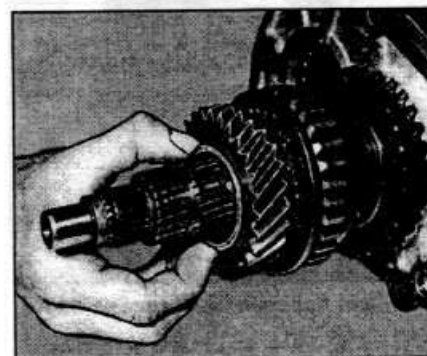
Снятие стопорной шайбы и двух стопорных полуколец шестерни II передачи
